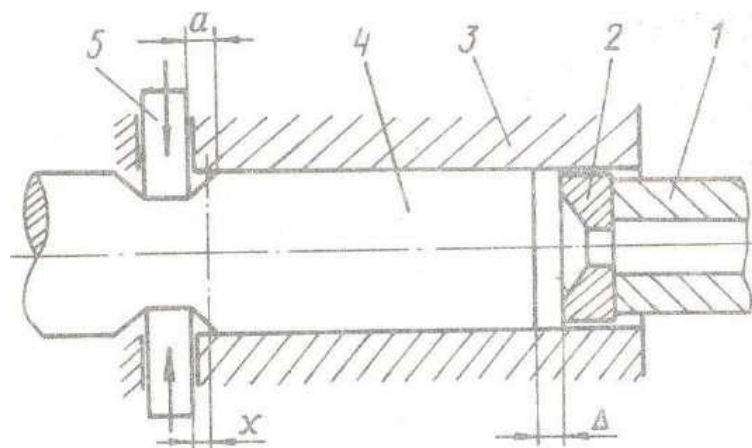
Инструментальная наладка установки проходного обратного прессования; 1 – полый пуансон; 2 – матрица; 3 – контейнер; 4 – заготовка; 5 – бойки.
